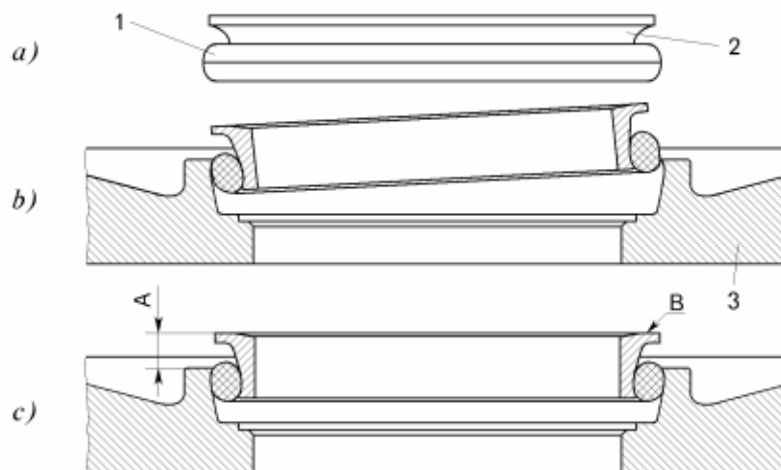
Установка торцовых резинометаллических уплотнений:
